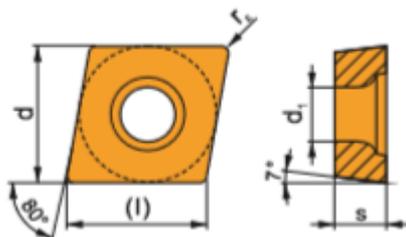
Пластина для черновой расточной головки ф. Pramet
